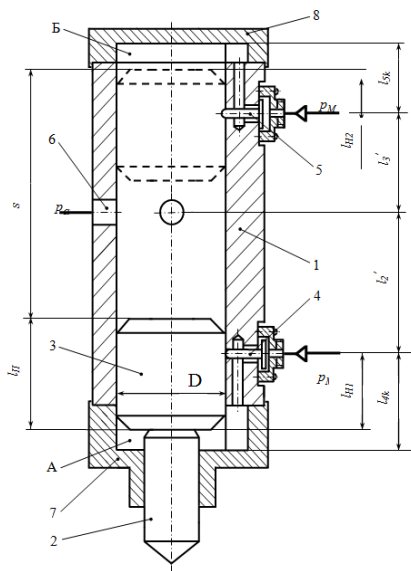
Конструктивна схема пневматичного привода з механічним зв'язком поршня-ударника з впускними елементами
